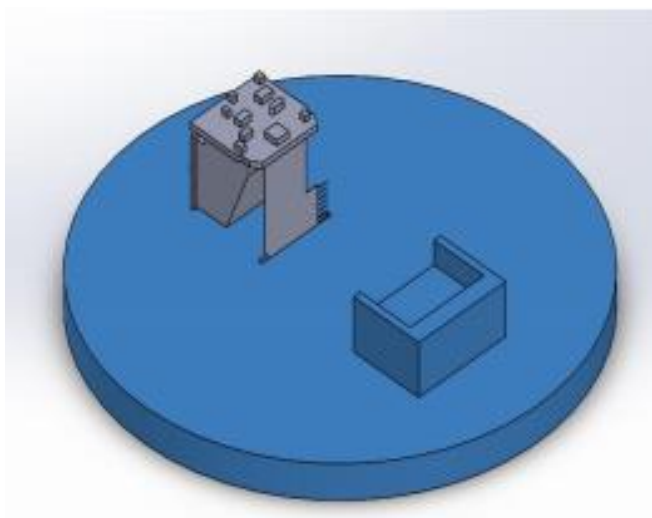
Fixture para operación de soldadura de L Flex, con Detector de Mainstream, vista 2.
